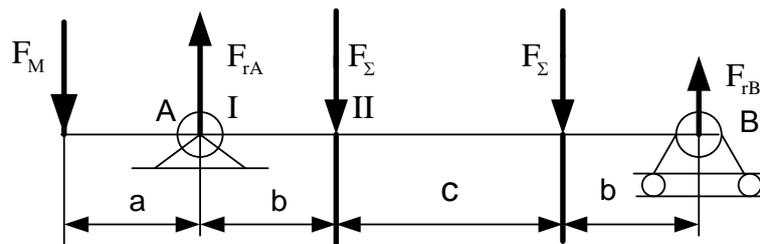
Расчётная схема для вала с двумя тяговыми звёздочками
